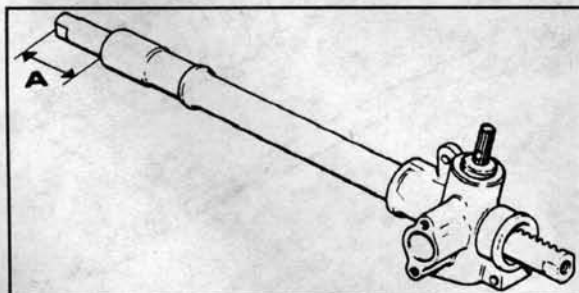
Подготовка собранного механизма (старая версия) для проведения регулировки
